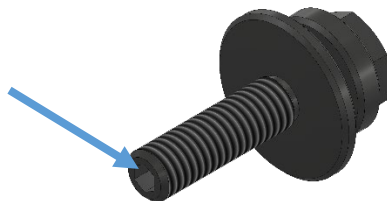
Position für Innensechskantschlüssel an der Cabinet-Schraube
